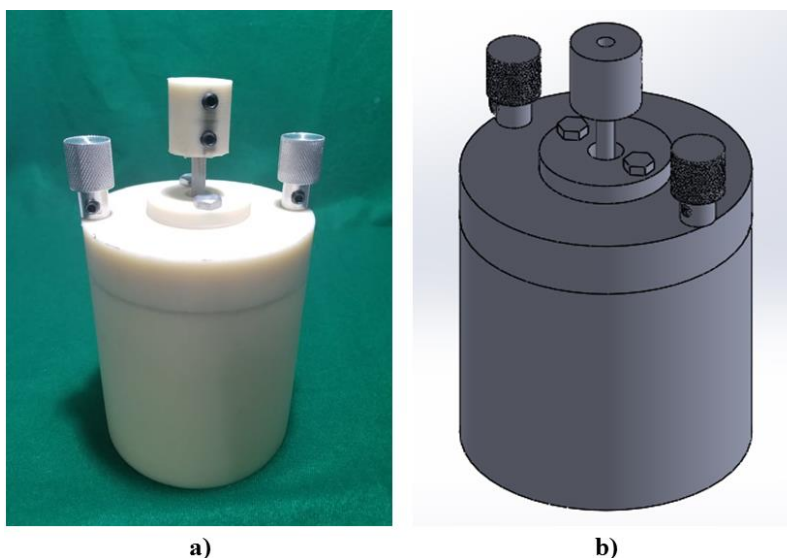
a) Mezclador de paletas inclinadas maquinado, b) Mezclador de paletas inclinadas diseñado.
